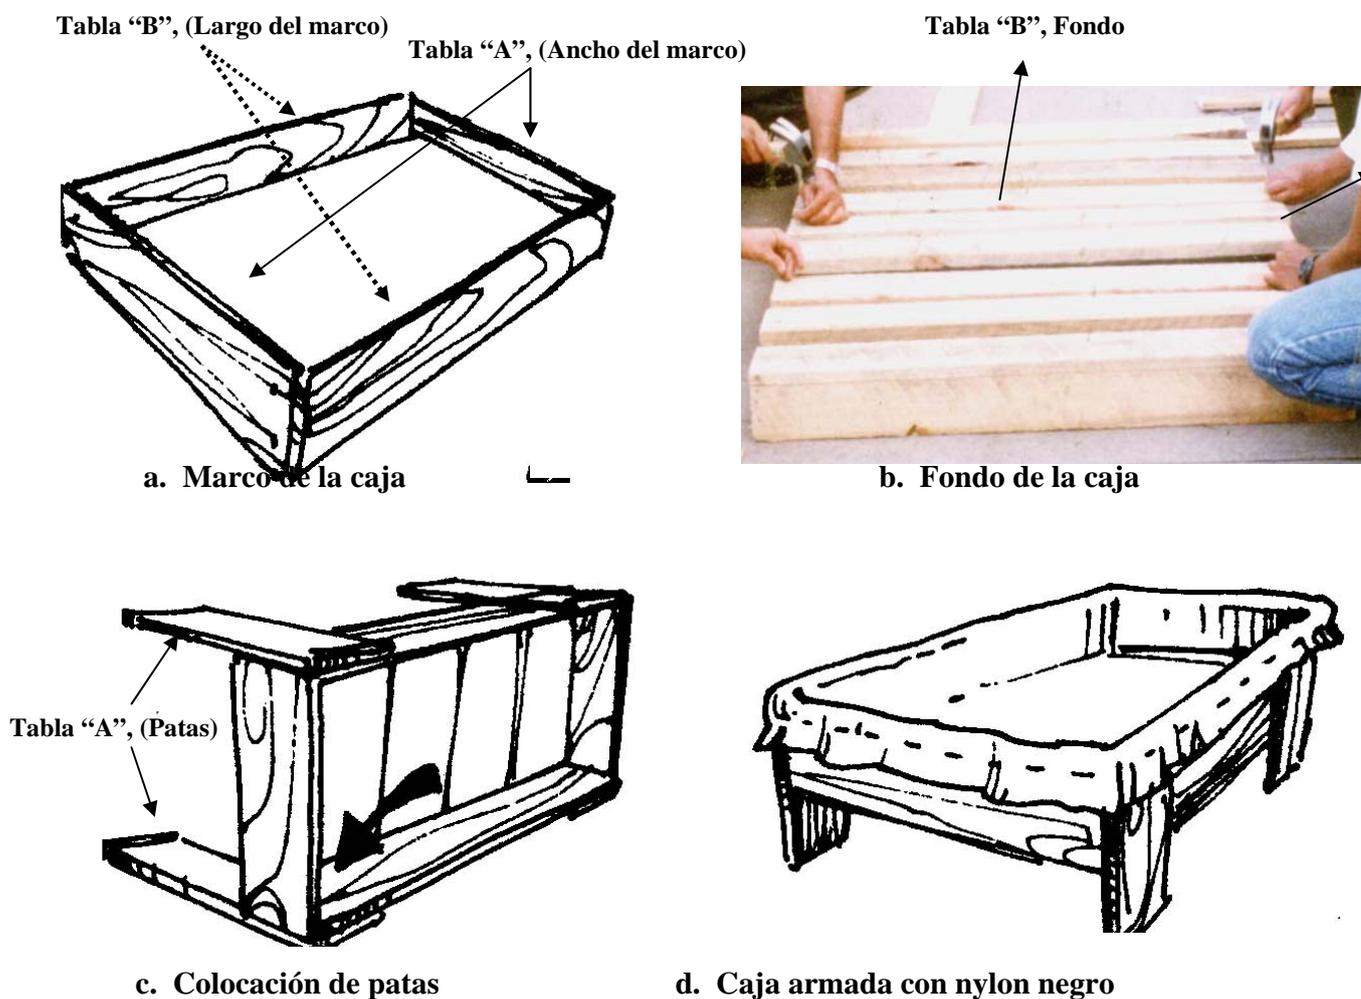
Armado secuencial de la caja para el ensayo de hidroponía.
